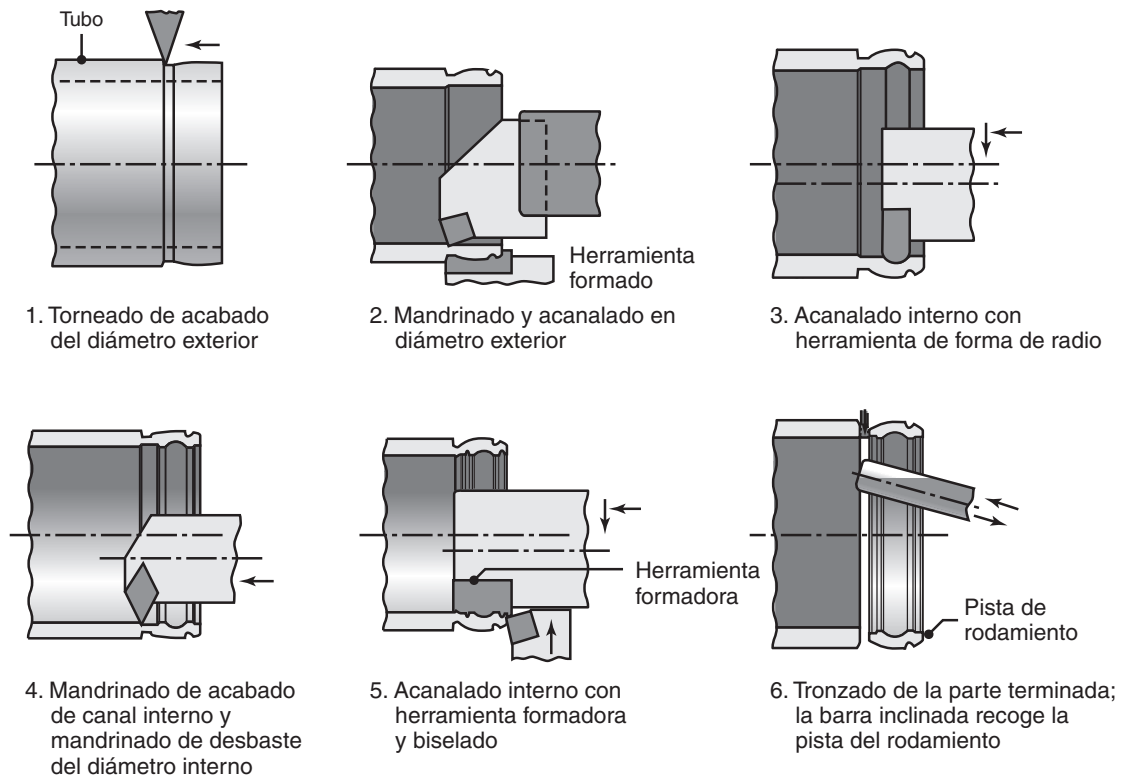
Maquinado de pistas exteriores de rodamiento.
